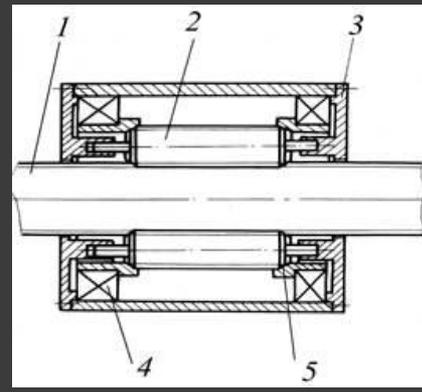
Передача винт – водило с резьбовыми роликами – конические кольца: 1 – винт; 2 – резьбовые ролики; 3 – водило; 4 – подшипники; 5 – конические кольца
